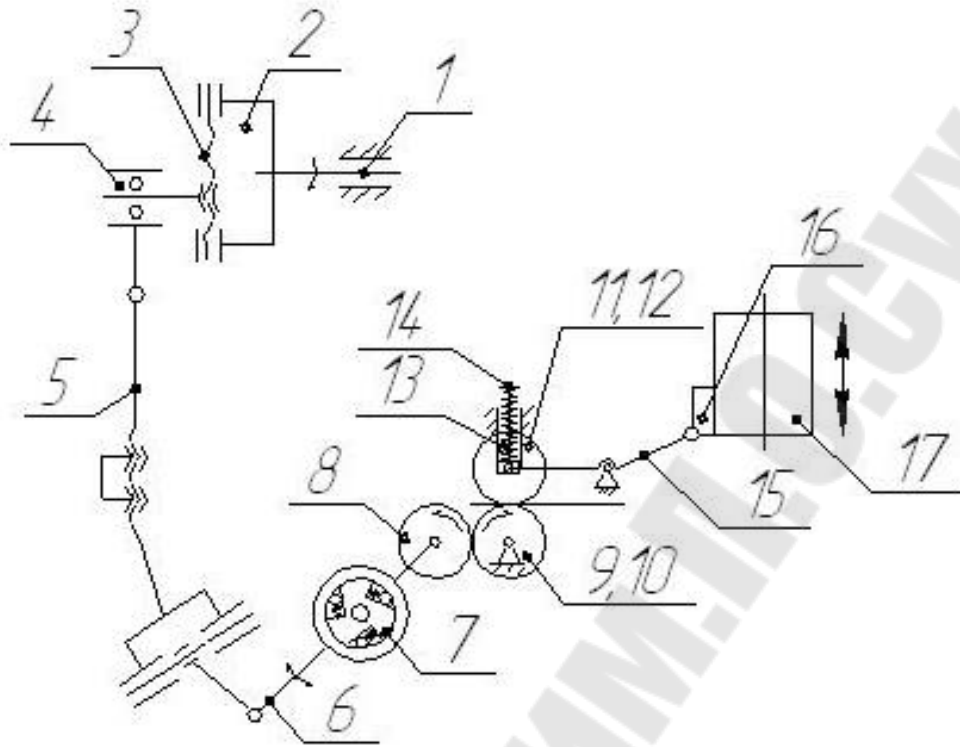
Кинематическая схема привода односторонней толкающей валковой подачи от главного вала прессы: 1- кривошипный вал прессы, 2-планшайба, 3-регулирующий винт, 4- кривошип, 5-тяги, 6-рычаг, 7-муфта обгона, 8,9,11-зубчатые шестерни,12,10- верхний и нижний подающие валки, 13-пружины,14- винт, 15-рычаг,16-кулачок, 17-ползун прессы.
